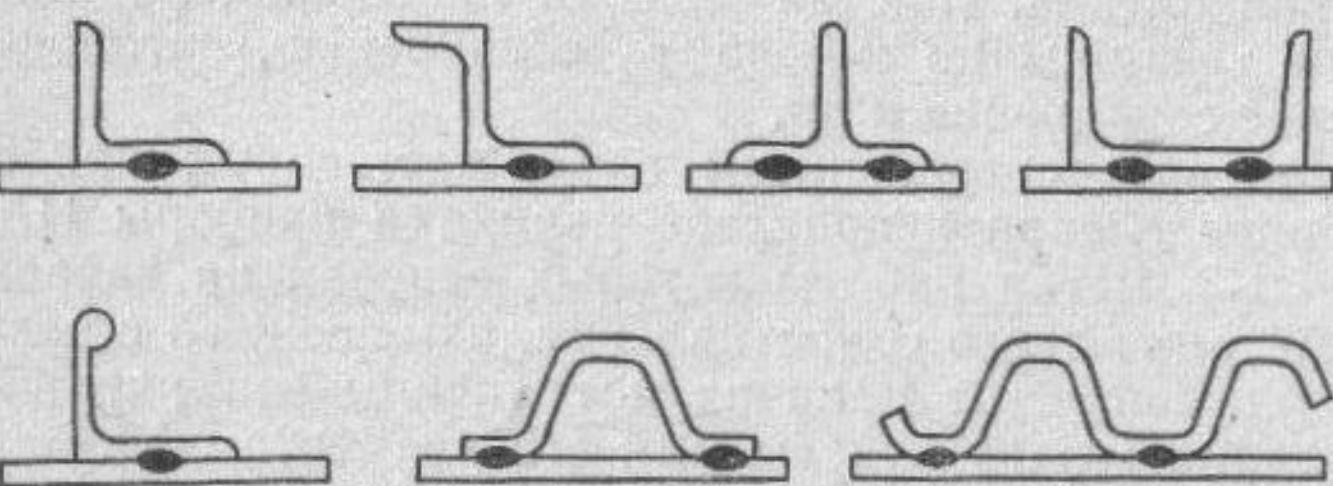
Рекомендуемые соединения для сварных и kleесварных каркасных конструкций.
